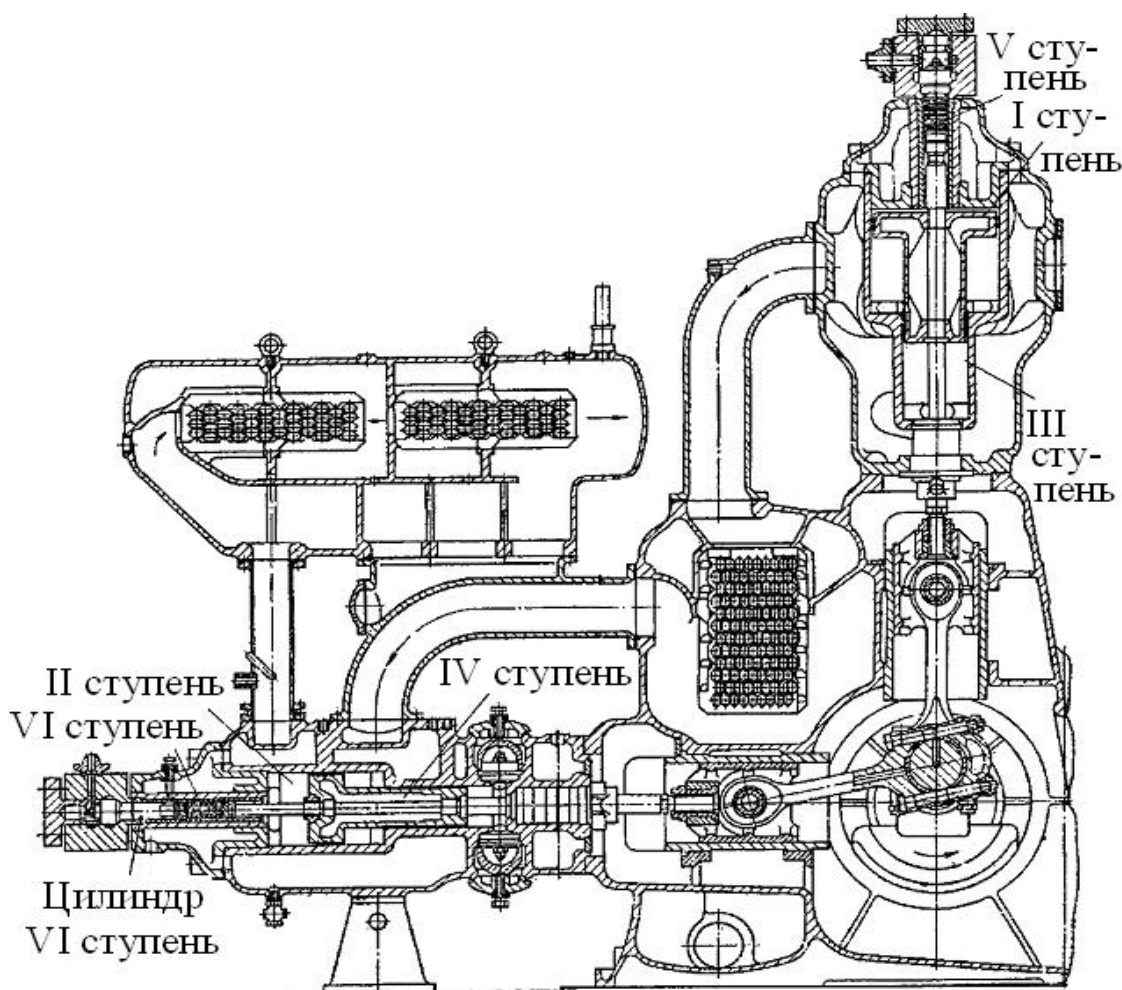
Угловой шестиступенчатый поршневой компрессор
